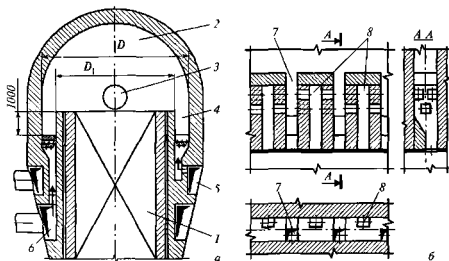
Форкамерная горелка бесшахтного воздухонагревателя ВНИИМТ: а — общий вид, б — газозвушнные каналы, 1 — насадка, 2 — купол, 3 — штуцер горячего дутья, 4 — форкамера, 5 — газовый коллектор, 6 — воздушный коллектор; 7 — канал для прохода газа, 8 — канал для прохода воздуха
